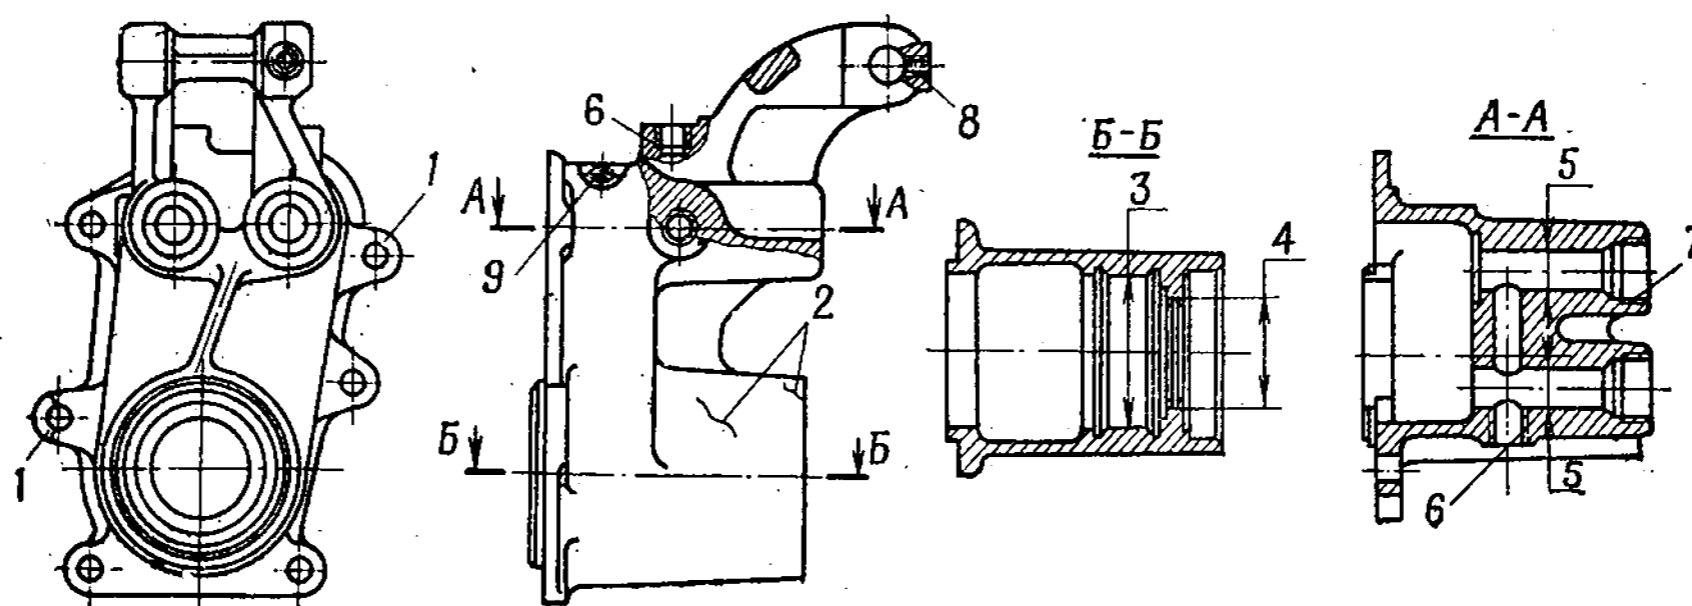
Картер штоков вилок переключения шестерен раздаточной коробки
